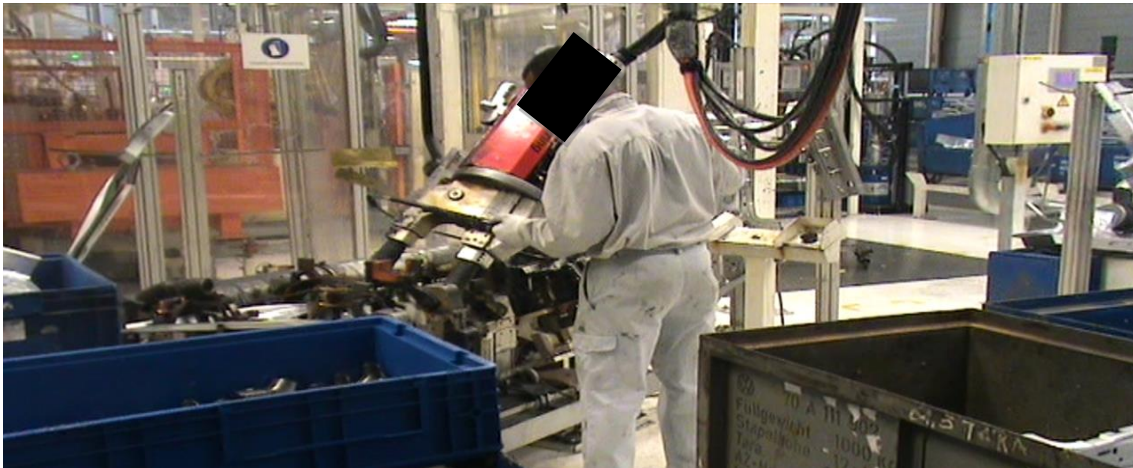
Situação I : Manipulação da pistola de soldadura
